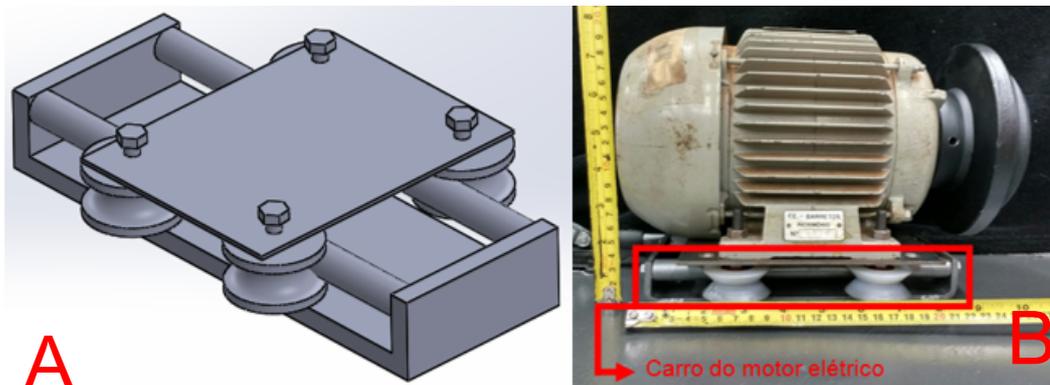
Projeto do carro para motor elétrico (A); conjunto motor/carro (B).
